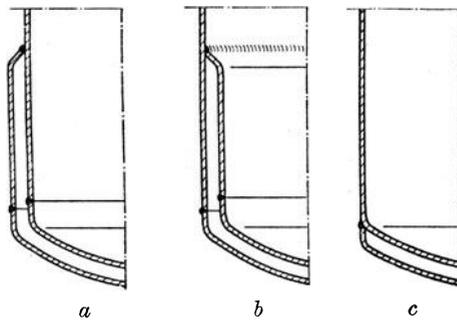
Schweißnähte an Doppelböden.
